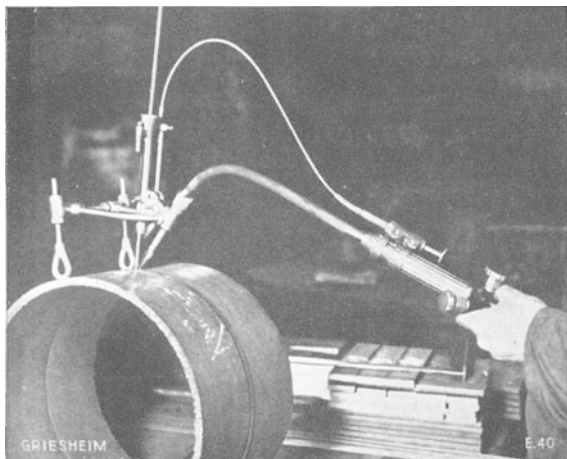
a. „Lindewelder“ Zweiflammen-Handschweißgerät.
